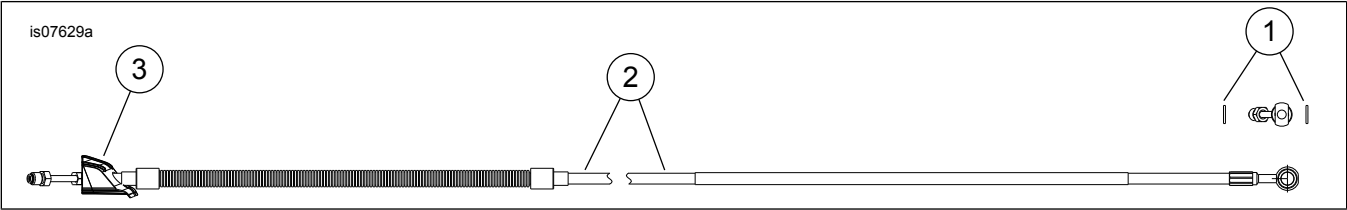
Peças de reposição: Kits de tubulação da embreagem hidráulica
